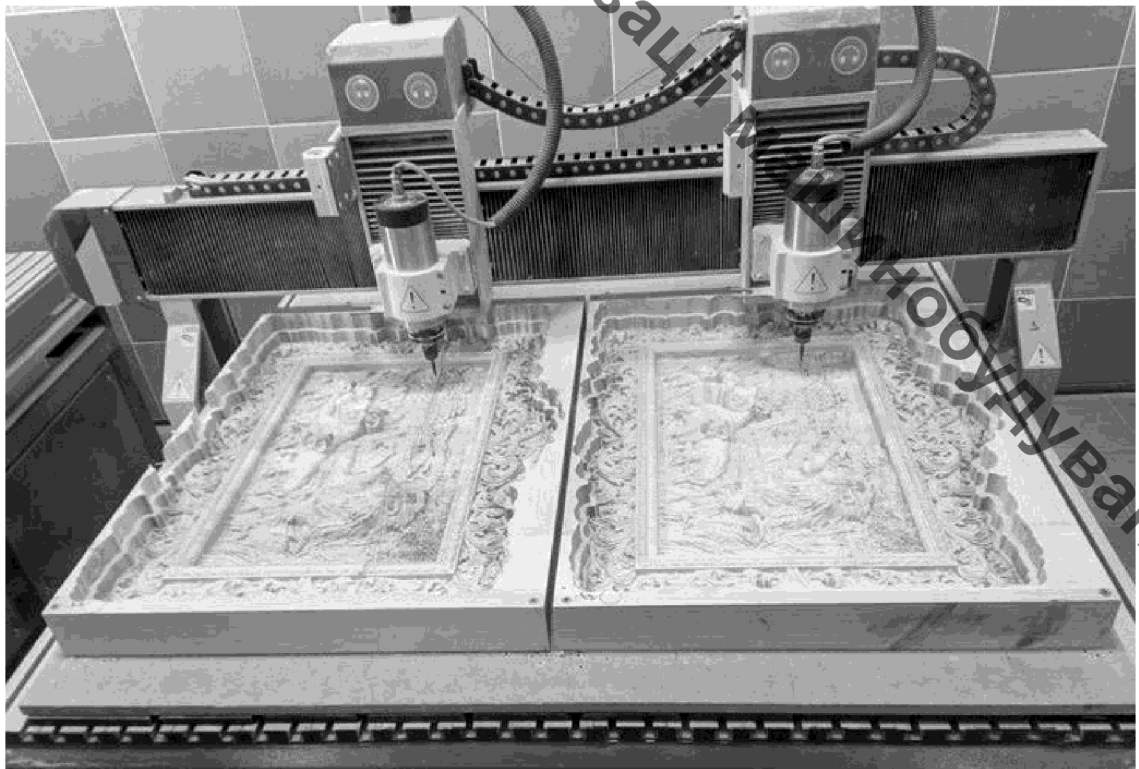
Обробка твердої породи дерева на фрезерно-гравірувальному верстаті з ЧПК
